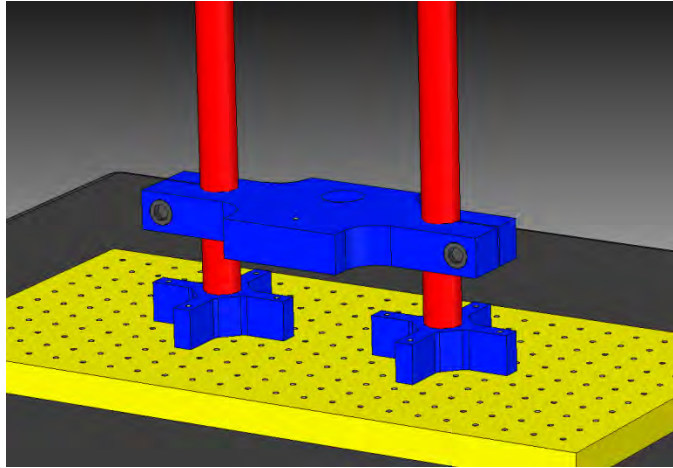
Cabezal fijo montado en columnas de estabilidad y estructura.
